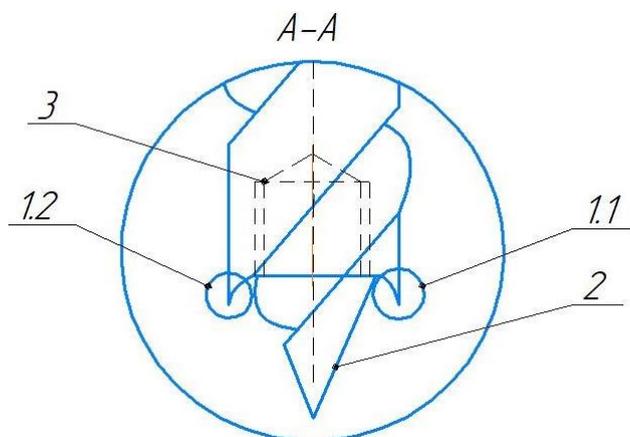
Сборная режущая часть Вид А рисунка 3б
